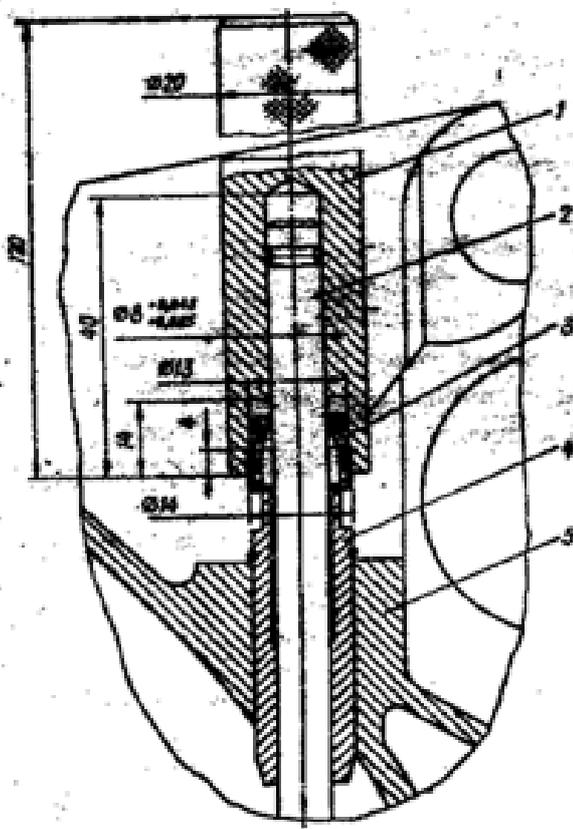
Оправка для запрессовки маслоотражательного колпачка клапана: 1 - оправка М9840-885; 2 - клапан или направляющий стержень; 3 - маслоотражательный колпачок клапана; 4 - направляющая клапана; 5 - головка цилиндров
